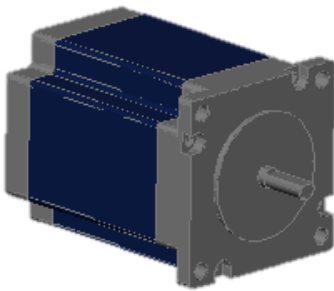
Συναρμολόγηση Ball Screw 3
